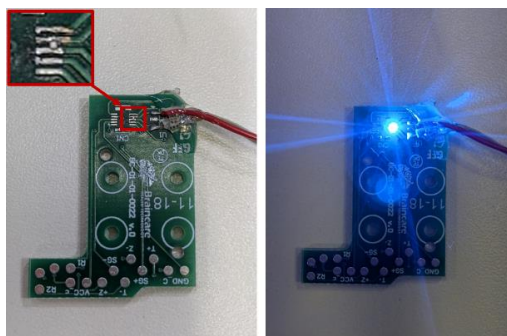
Placa de circuito com o uLED soldado entre dois pads.
